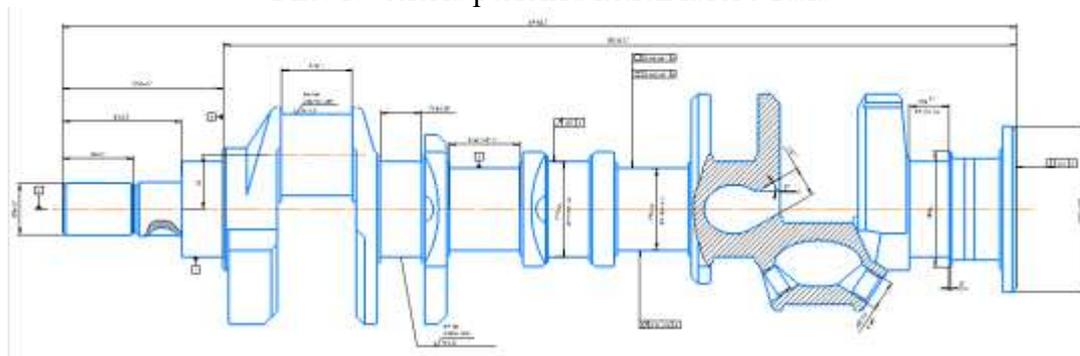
Коленчатый вал двигателя ЗМЗ-511
